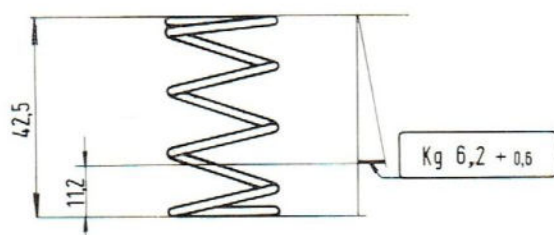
Prüfwerte der Feder des Ausrückkolbens.
